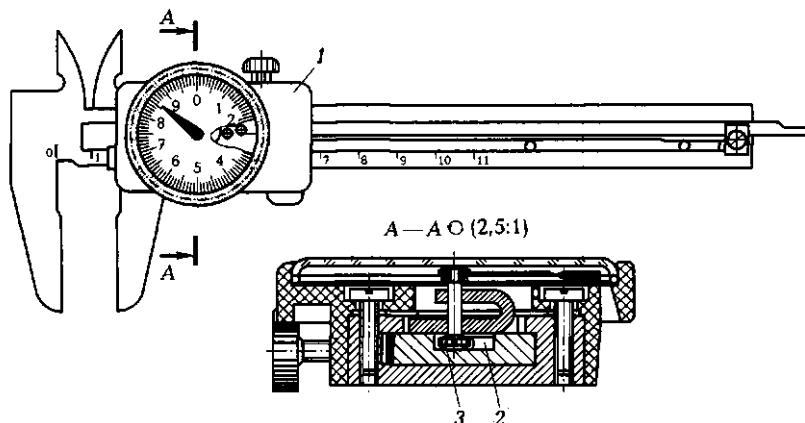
Конструкция индикаторного штангенциркуля:
